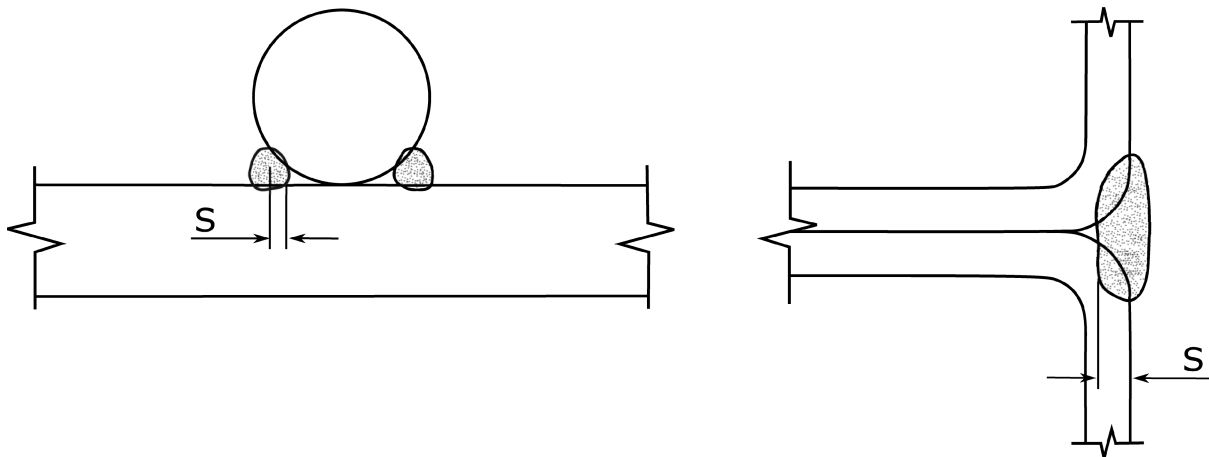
Eindringtiefe „s“ für Bördelnähte
